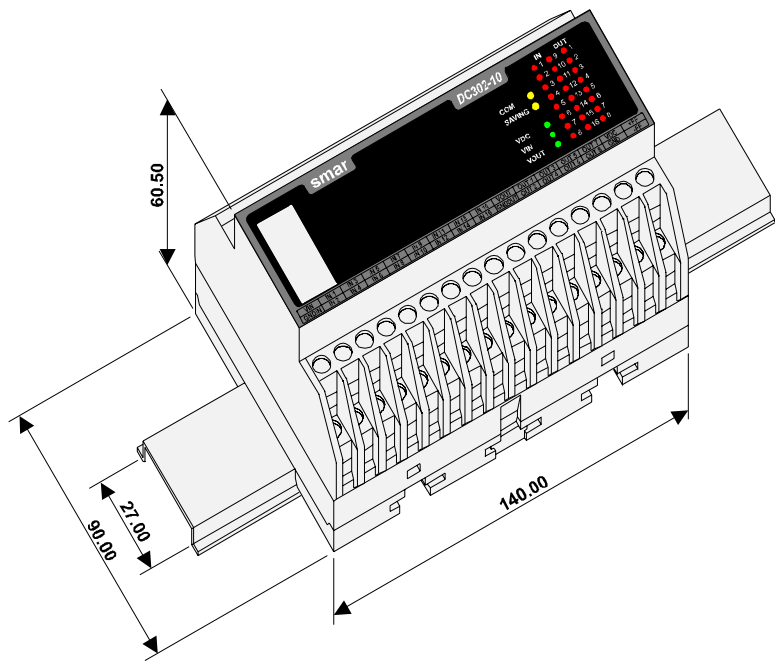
Montagem Mecânica e desenho dimensional do DC302
